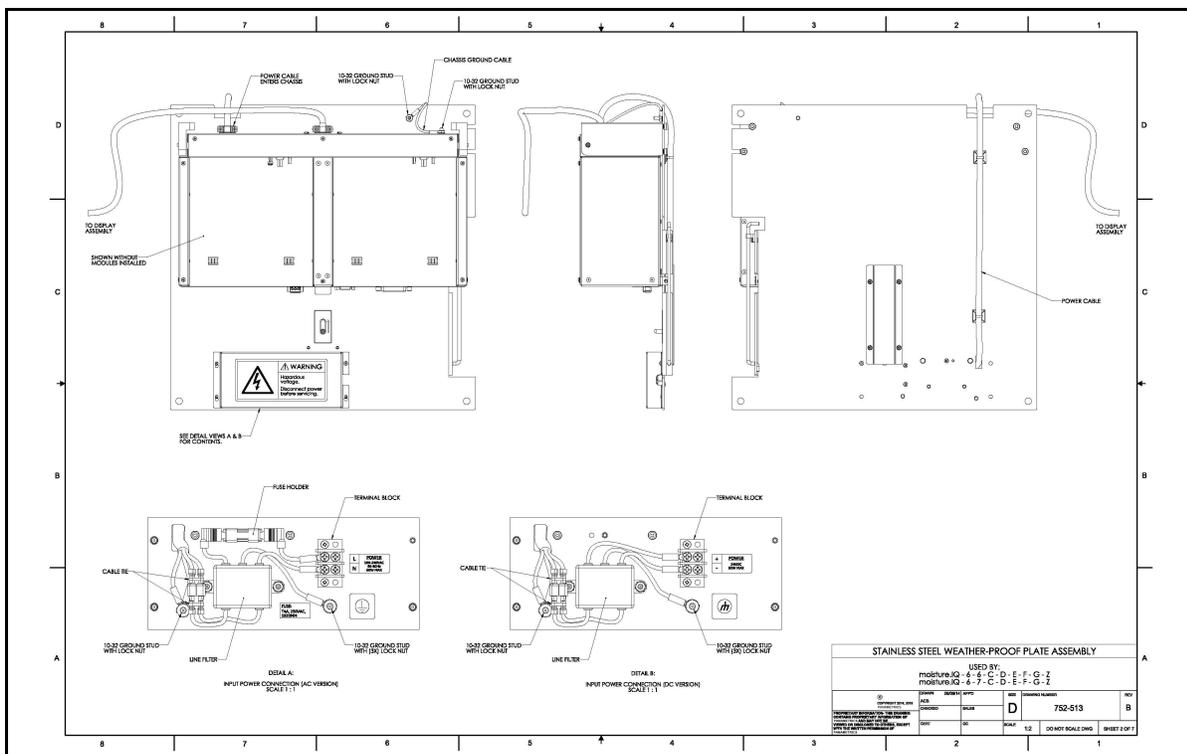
Montageplatten-Baugruppe für wettergeschützte Version (Zeichnung 752-513_revB, Blatt 2 von 5)
